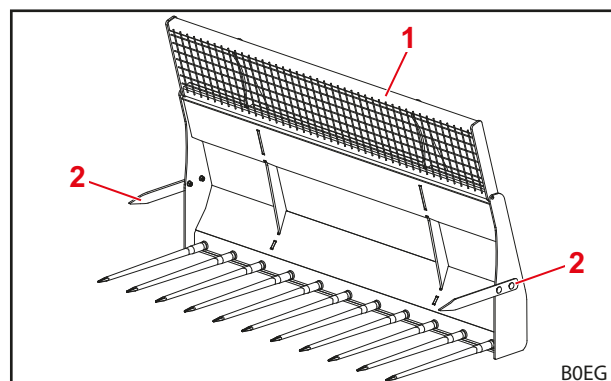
Konstrukcija vilice za stajsko gnojivo (za prednje utovarivače FZ 60/60.1/80.1/100) – pogled straga
